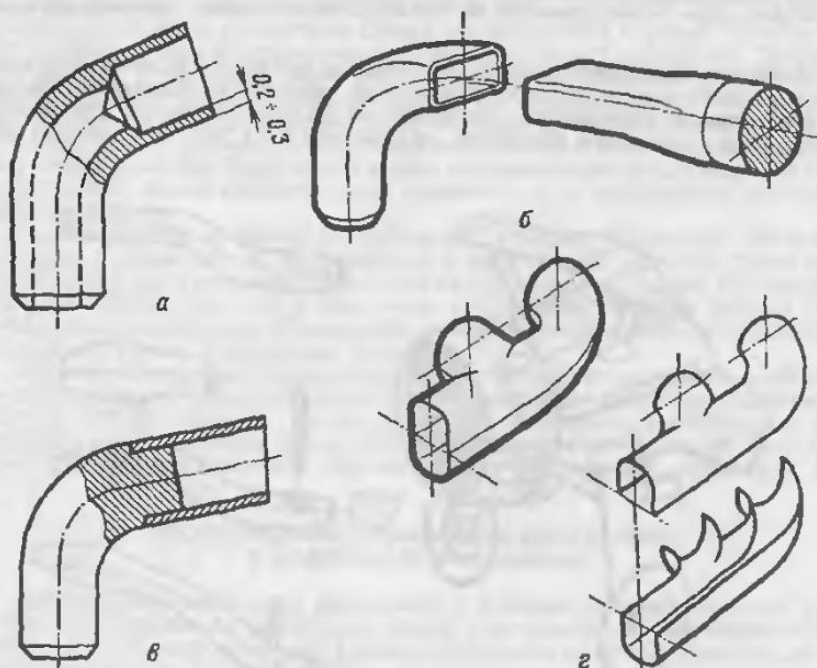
Изготовление выхлопных патрубков: а - рассверловкой; б - на оправке; в - напайкой, г - штамповкой
